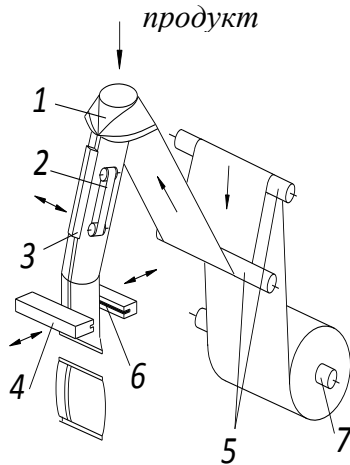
Компонування машини нахиленого типу: 1 – рукавоутворювач; 2 – механізм протяжки; 3 – механізм поздовжнього зварювання; 4 – механізм поперечного зварювання; 5 – механізм подачі плівки; 6 – механізм відрізання; 7 – рулонотримач
